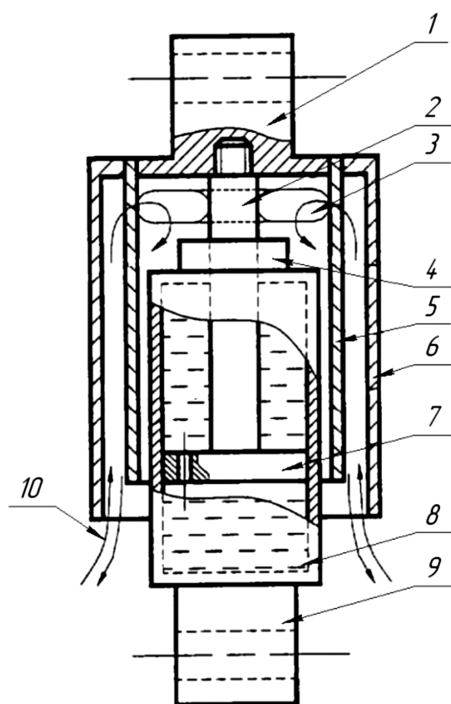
Гаситель колебаний с отверстиями в защитном кожухе: 1 — верхняя проушина; 2 — шток; 3 — отверстия во внутреннем кожухе; 4 — защитные уплотнения; 5 — внутренний защитный кожух; 6 — внешний защитный кожух; 7 — поршень; 8 — корпус гасителя; 9 — нижняя проушина; 10 — направления движения воздуха.
